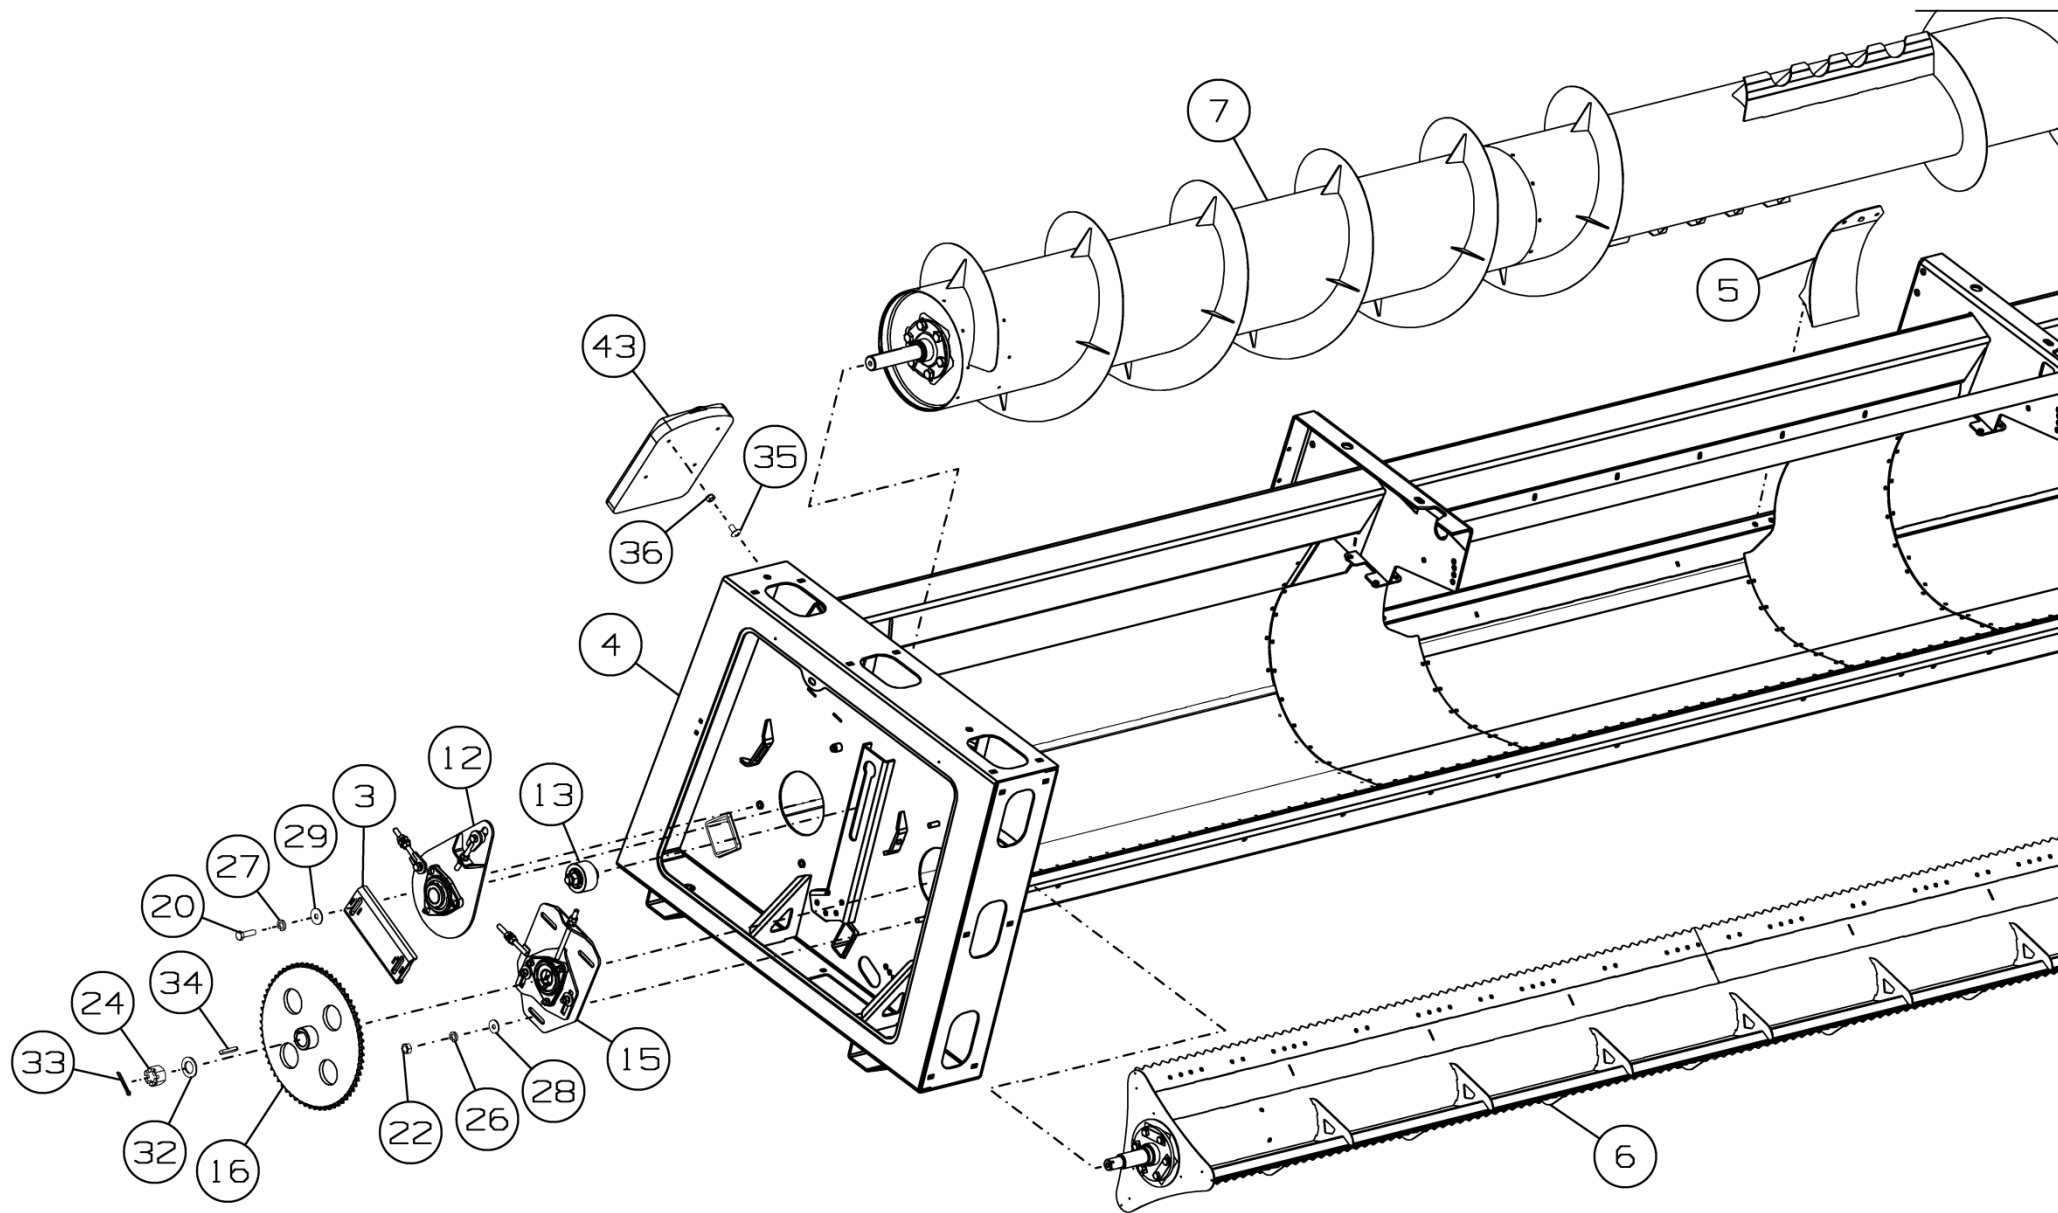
Корпус жатки SS-490.01.01.000-03 (правая сторона)
